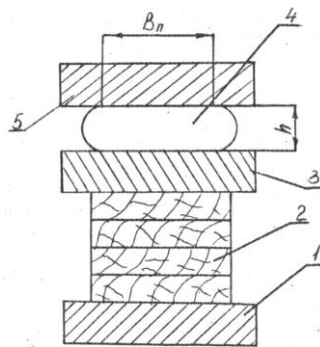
Схема пресування блока в пневматичному пресі: 1 - нерухома опора; 2 - склеюваний блок з чотирьох брусків; 3 - рухома плита; 4 - пневмокамера; 5 - нерухома плита
